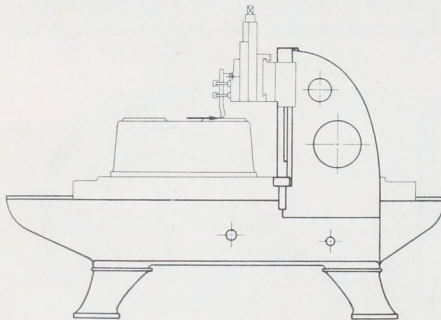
Hobelmaschinenständer mit parabolisch begrenztem Werkzeugträger.
